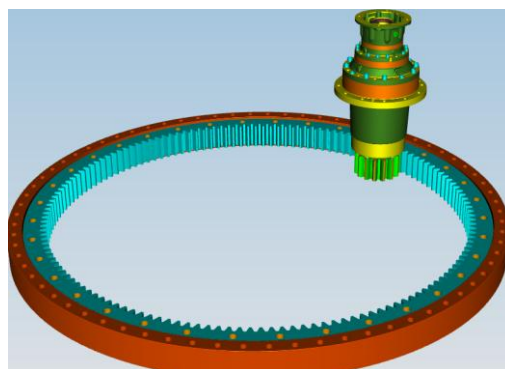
Detalle de un reductor sobre el rodamiento de giro
